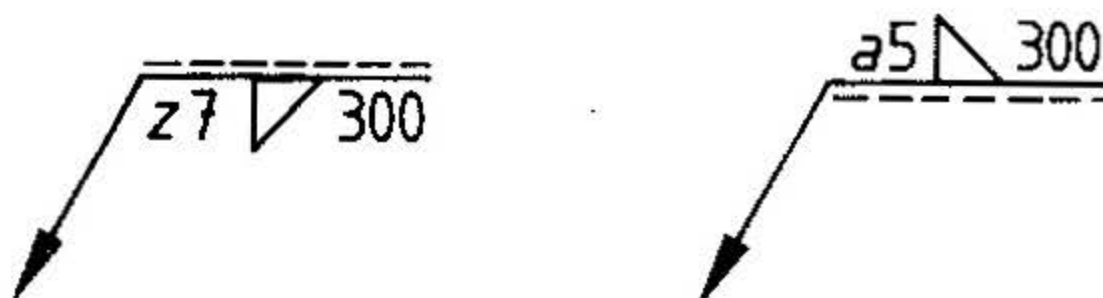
Soldadura por el lado de la flecha
